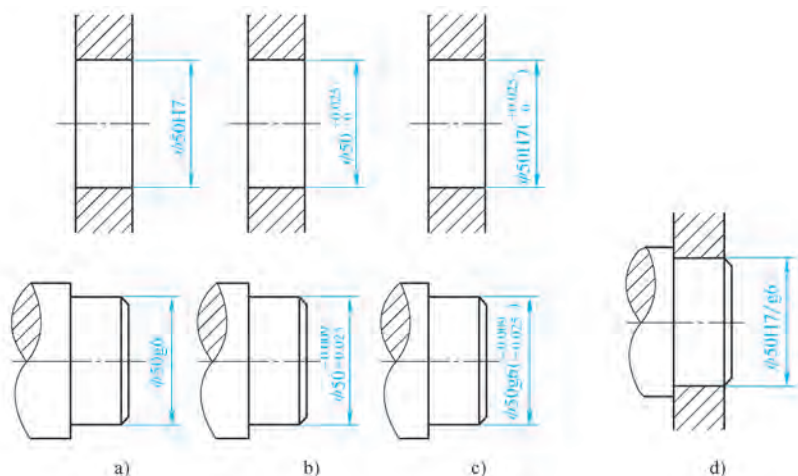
尺寸公差与配合在技术图样上的标注
